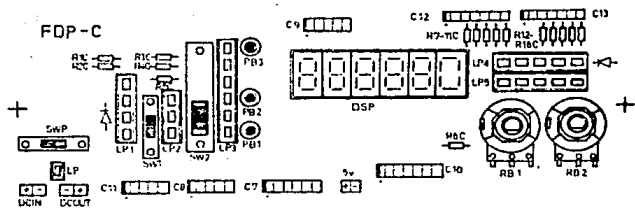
Ensemble de composants tarjeta FDP-C.
